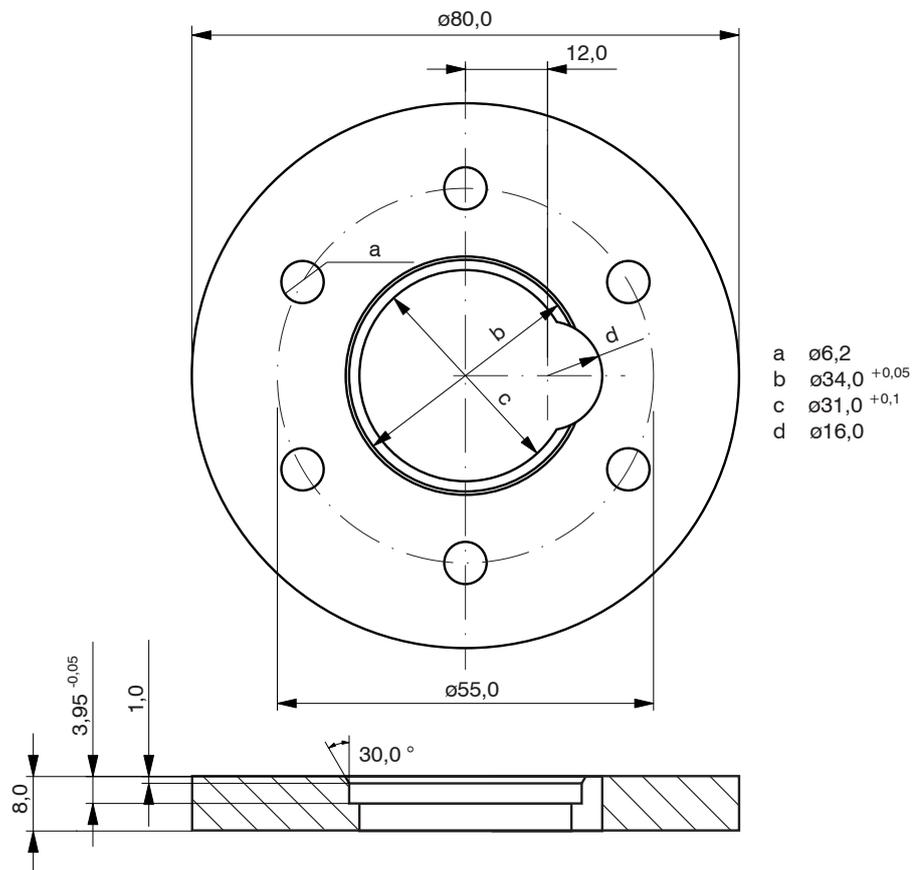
Bague de montage pour capteur, série EDS- ... -S, dimensions indiquées en mm, pas conformes à l'échelle
